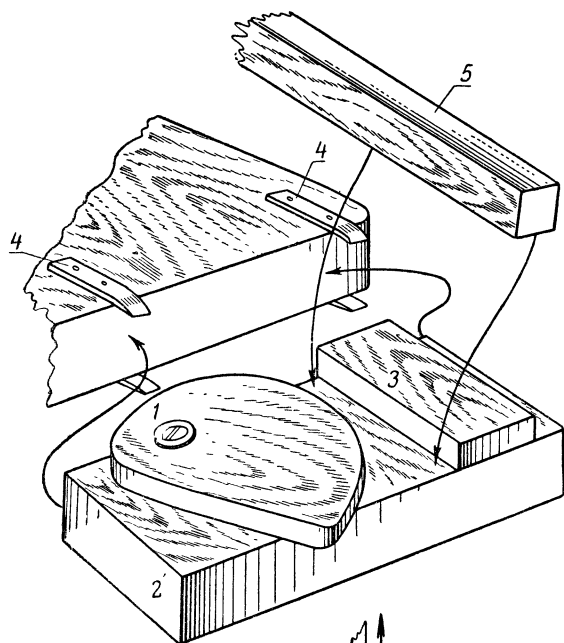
Способ изготовления легкого и прочного колеса.
